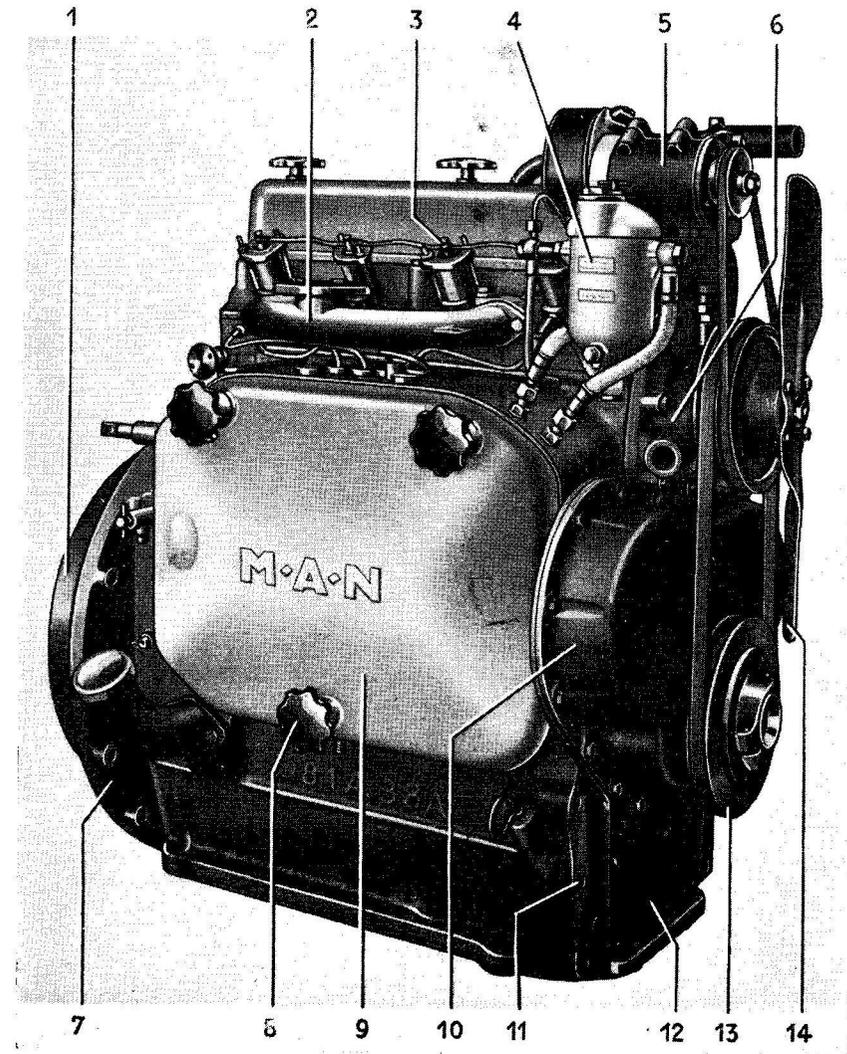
Motor, Ansicht auf Einspritzpumpenseite
